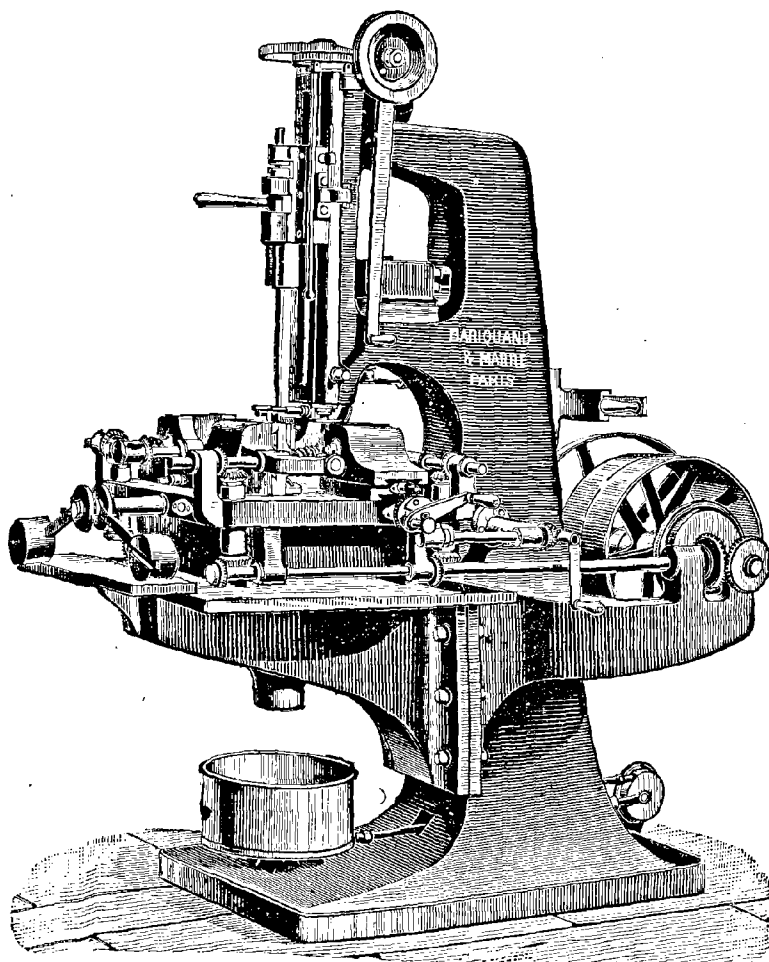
Machine à fraiser quadruple de Bariquand et Marie.
